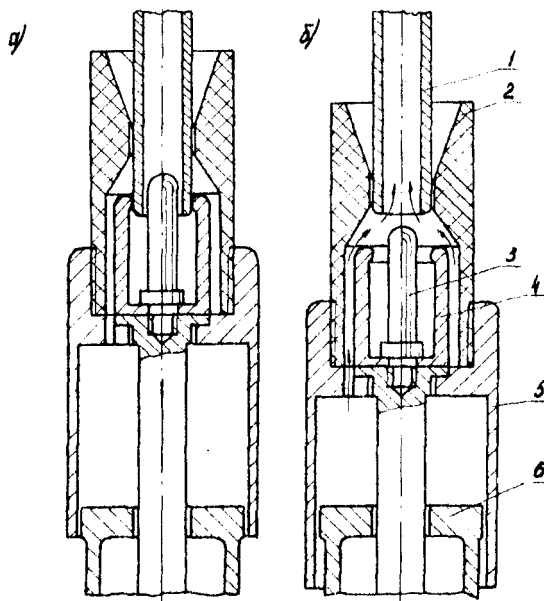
Автопневматичний дугогасний пристрій
